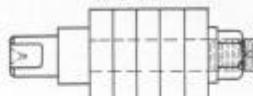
Mandril de tuercas para el acabado de discos para engranajes.
